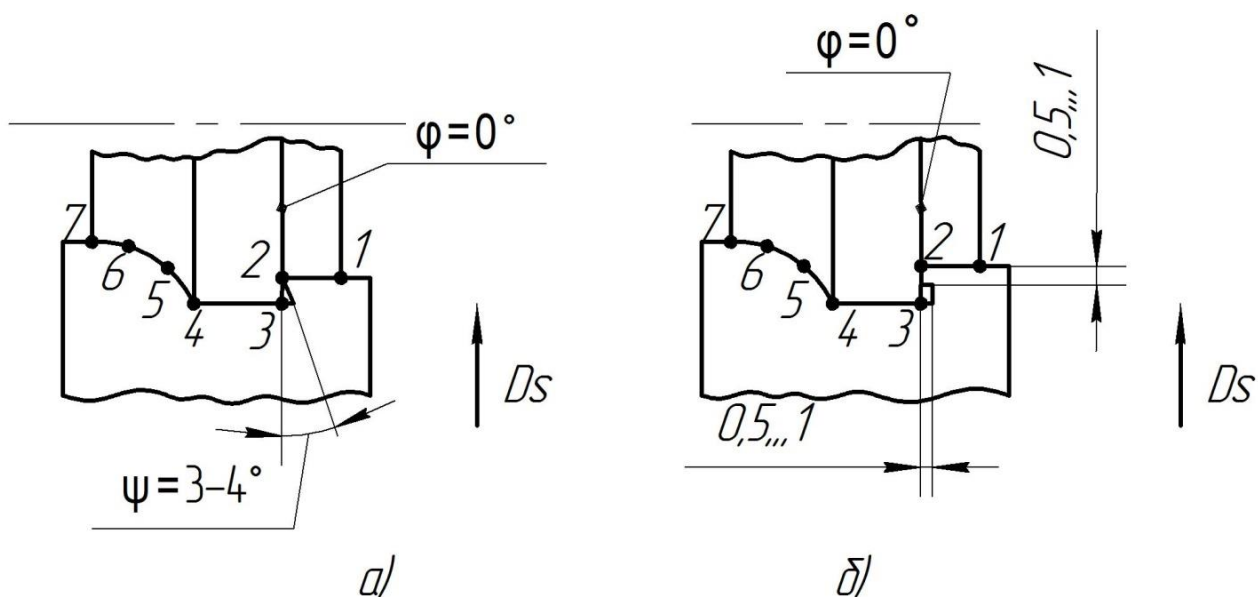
Оформление дополнительных режущих кромок для подрезки торцевой поверхности:
